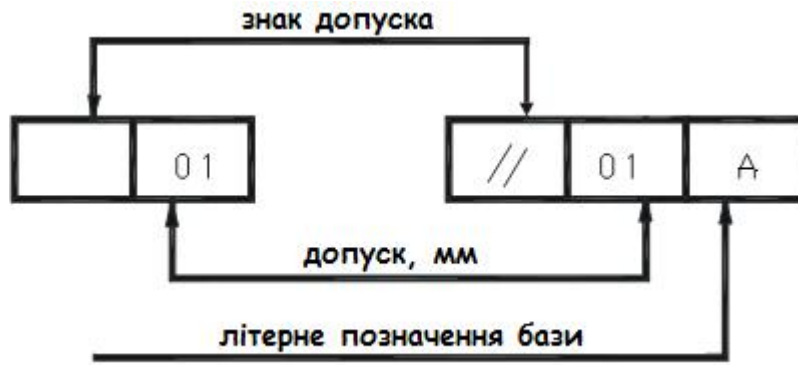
Приклад позначення допусків форми і розташування
